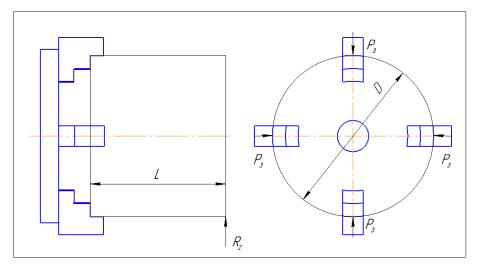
Консольная заготовка в четырех-кулачковым патроне
